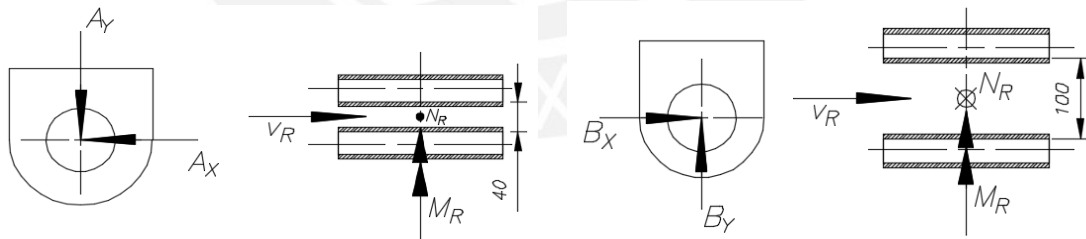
DCL cordón de soldadura de los soportes A (Izquierda) y B (derecha)
